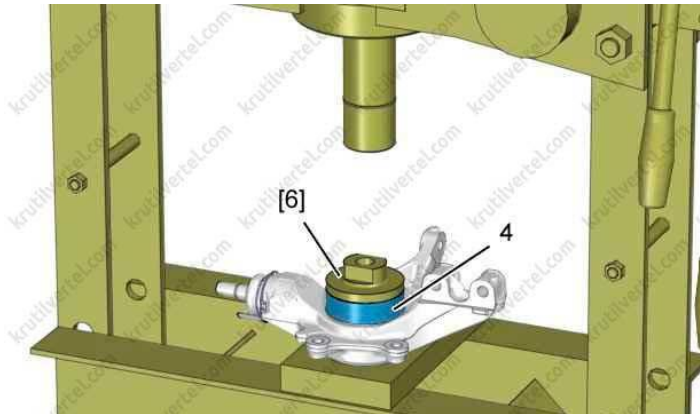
Запресування підшипника в цапфу: 1 – оправка.
